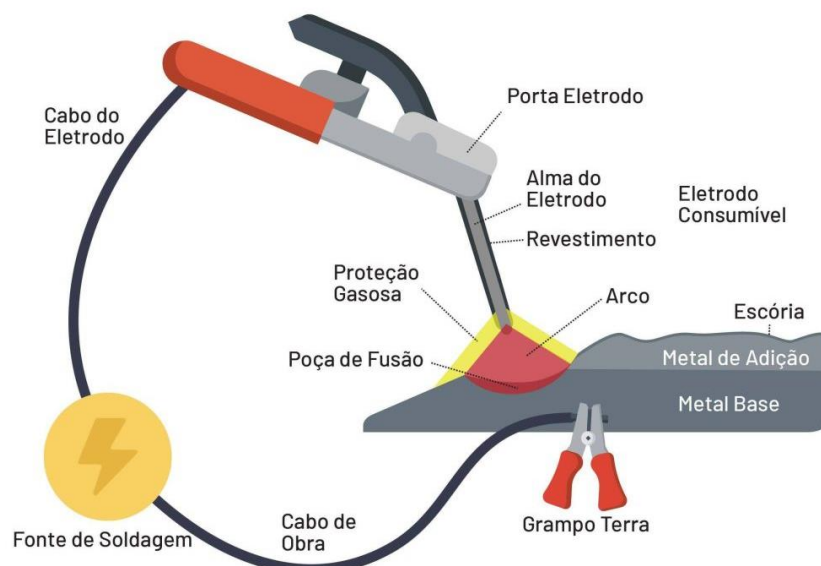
Desenho representativo da soldadura por eléctrodo revestido (SMAW) [13].
